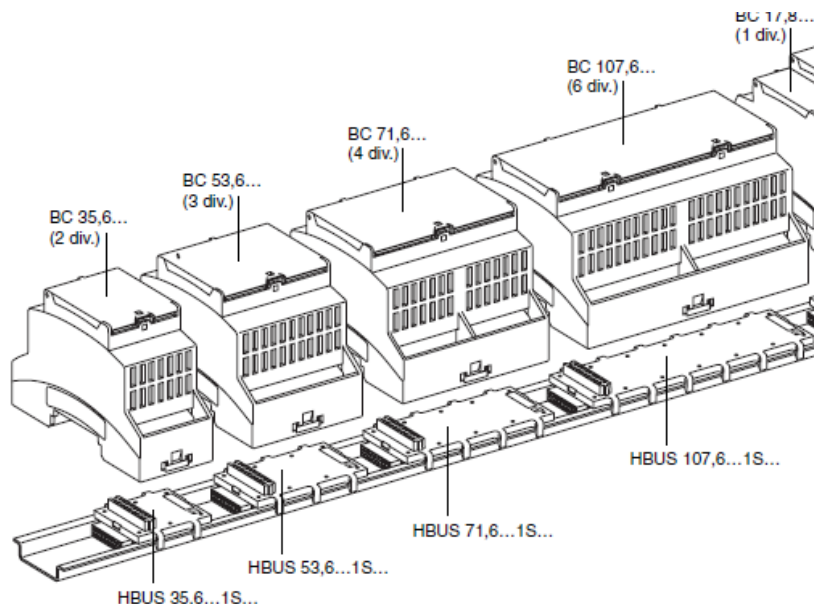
Установка контроллера UNI704 и модулей на DIN-рейку
